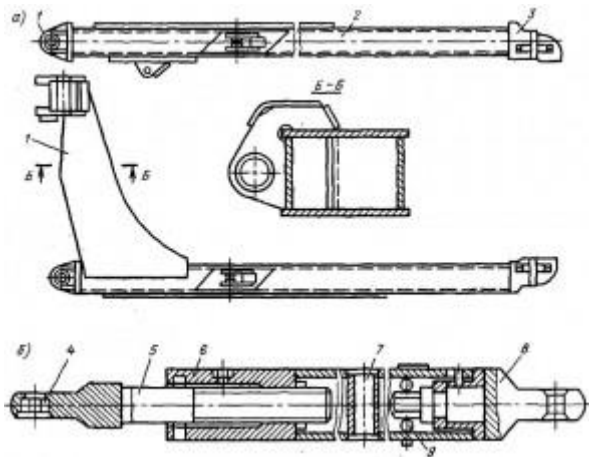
Толкающие устройства в бульдозерах с неповоротным отвалом: а — толкающее устройство: 1 — кронштейн; 2 — толкающий брус; 3 — опора; б — раскос: 4 — подшипник; 5 — винт раскоса; 6 — труба (раскос); 7 — патрубок; 8 — проушина раскоса; 9 — стопор
